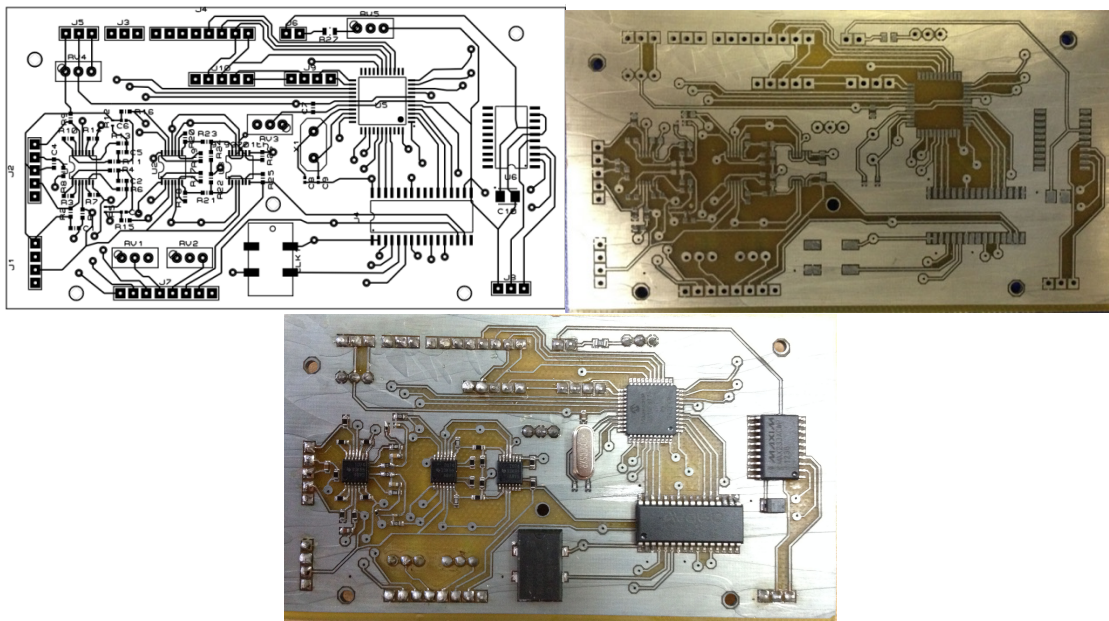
38 Diseño de circuitos, tarjeta fabricada y componentes colocados
